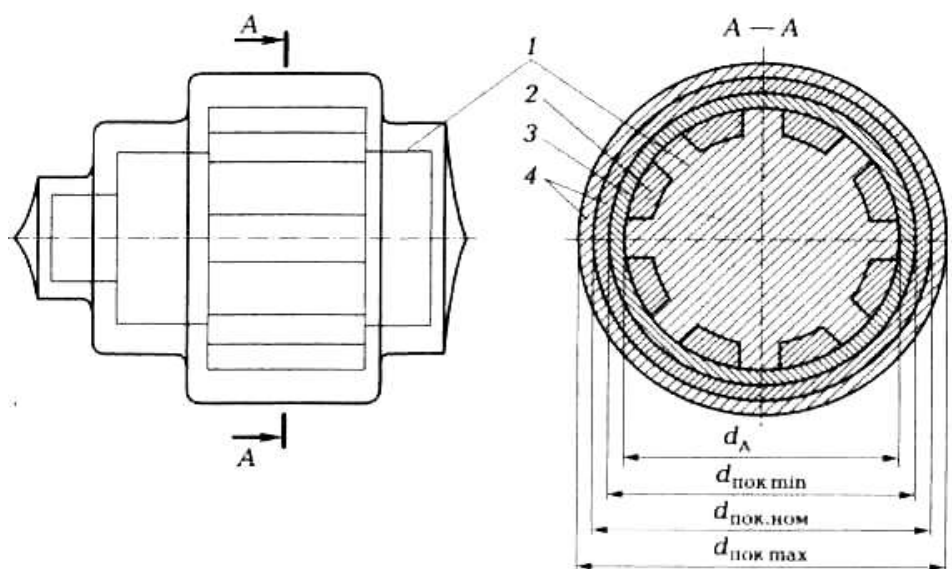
Чертеж поковки для детали с основными размерами, напуском, припуском и допуском: 1 — готовая деталь; 2 — напуск; 3 — припуск; 4 — допуск; d_k и d_m — диаметры детали и поковки (минимальный, номинальный и максимальный)
